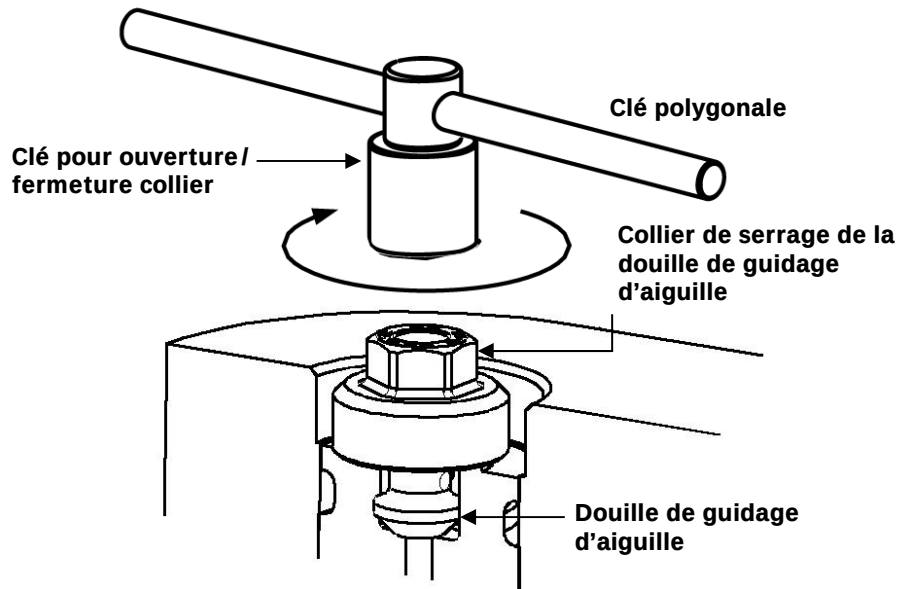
Assemblage de la douille de guidage d'aiguille et du collier
